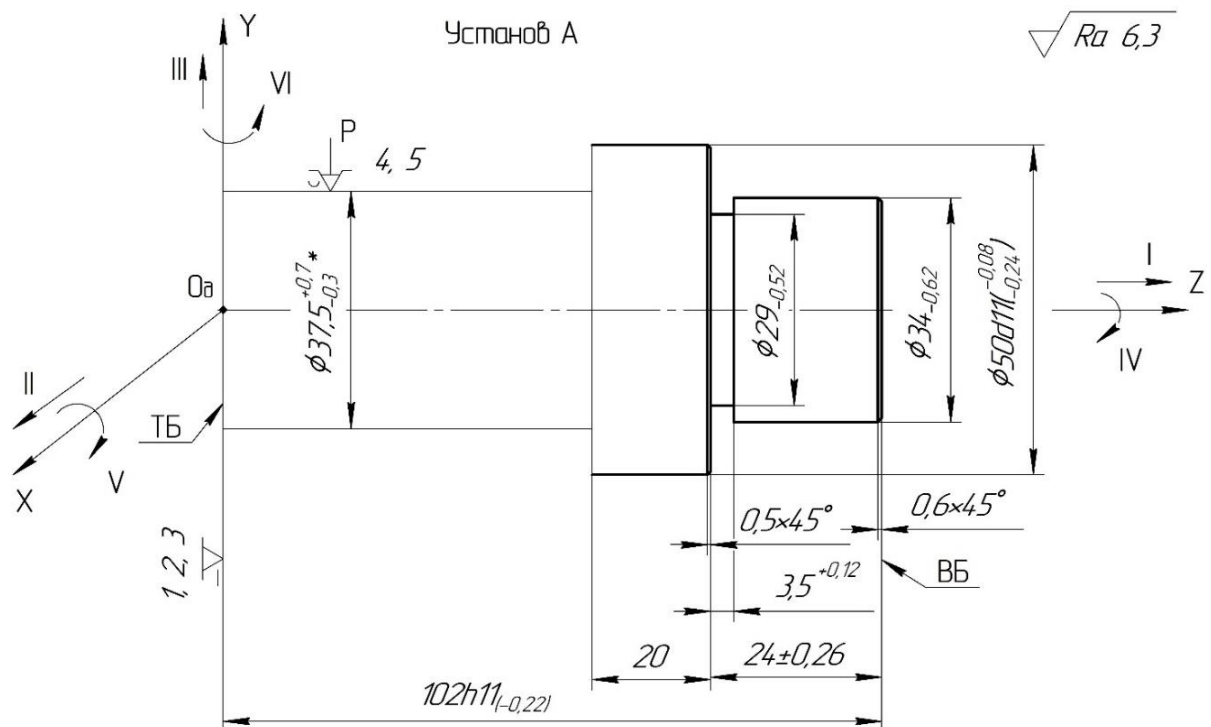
Базування заготовки на операції 015 «Токарна з ЧПК». Схема №1
